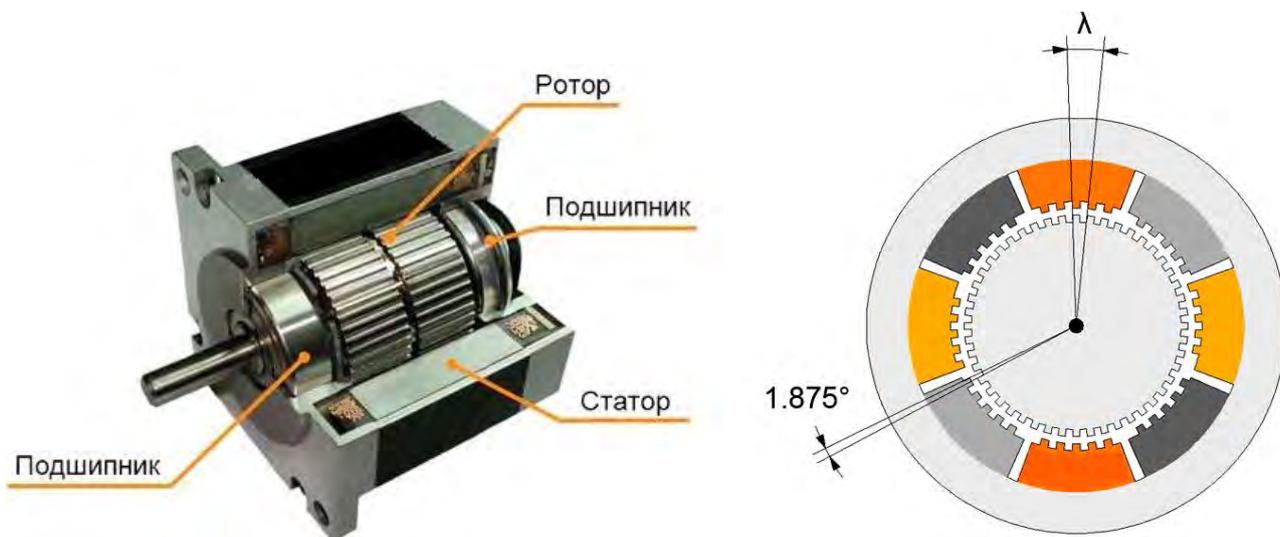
Шаговый двигатель: λ – зубцовое деление; $1,875^\circ$ – шаговый угол
